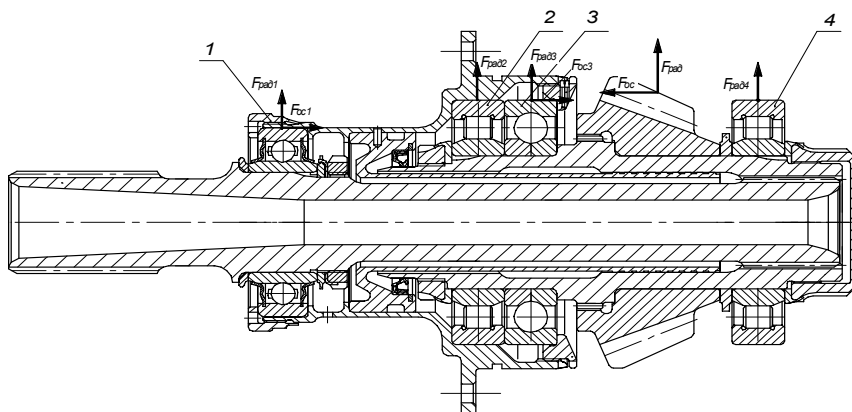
Схема действия сил на подшипники ведущей шестерни хвостового редуктора
